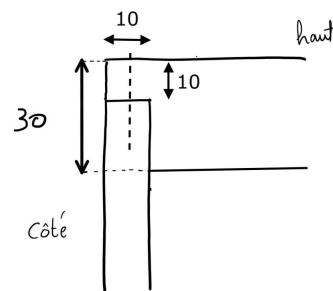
Fixation des plaques de côté à la plaque du haut
